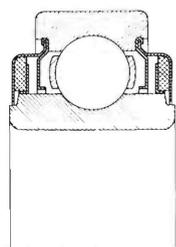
Rillenkugellager mit beidseitiger Filzringabdichtung.
